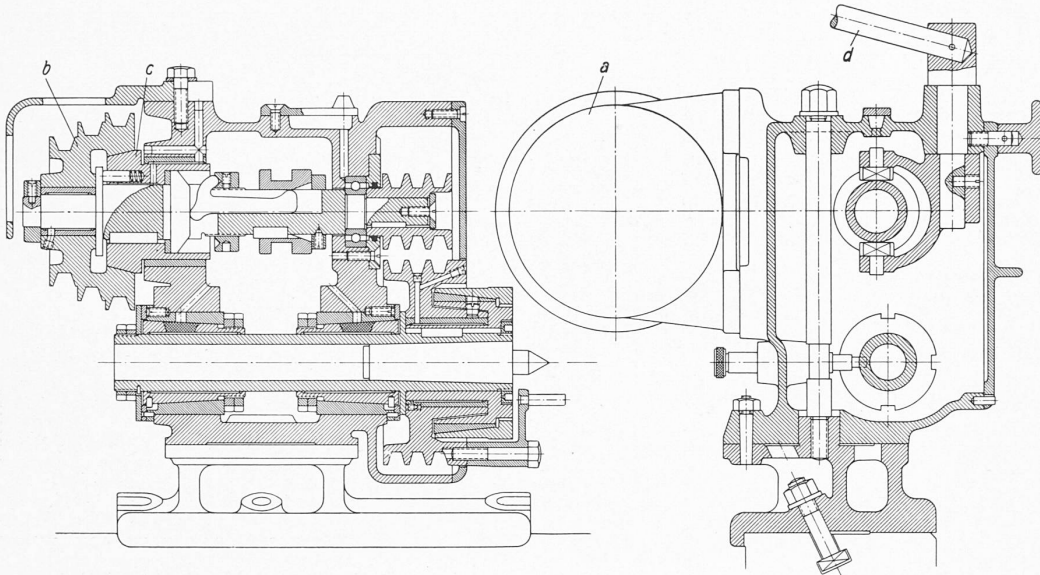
Werkstückspindelstock der kombinierten Rund-, Innen- und Planschleifmaschine (Kellenberger Werkzeugmaschinenfabrik).
